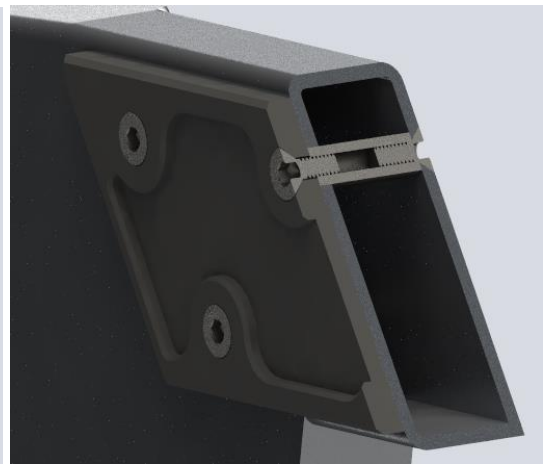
Vista seccionada de la viga con la placa atornillada
